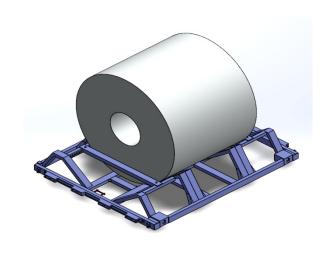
钢制座架装载卷状货物 Fig.3 Steel seat frame loading coiled cargo
